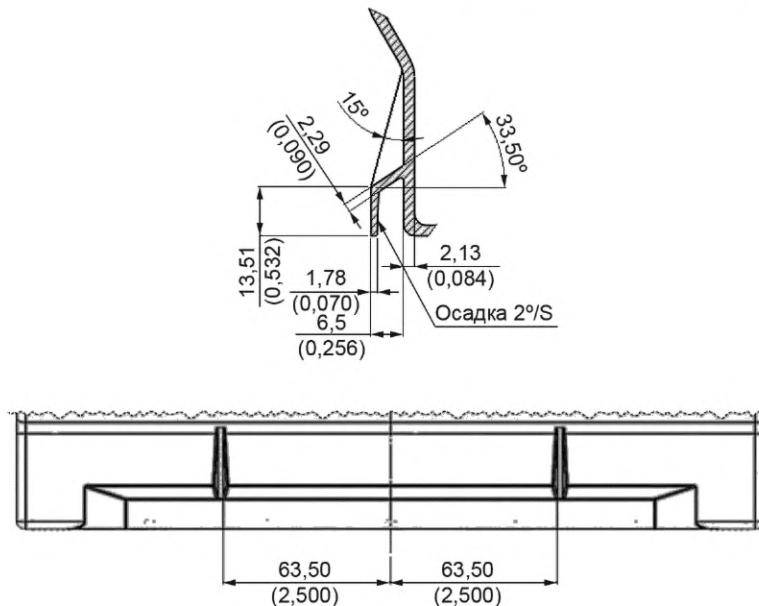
Форма и размеры бортиков на длинной стороне батареи
